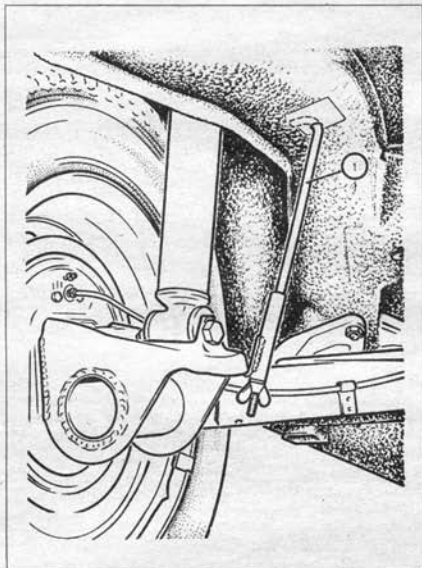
Установка штанги при регулировке привода регулятора давления:
